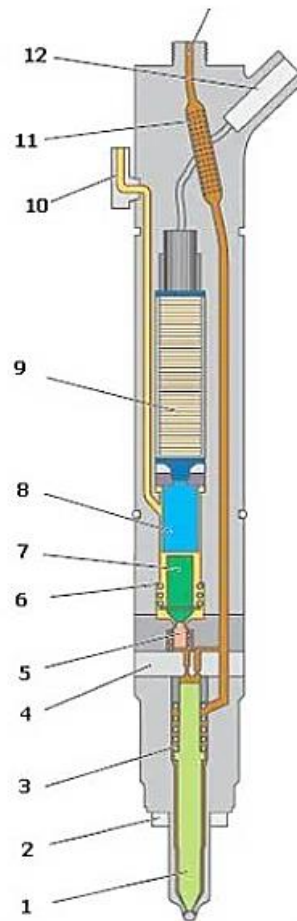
Конструкція п'єзофорсунки: 1 – голка форсунки; 2 – ущільнення; 3 – пружина голки; 4 – блок дроселів; 5 – перемикаючий клапан; 6 – пружина клапана; 7 – поршень клапана; 8 – поршень штовхача; 9 – п'єзоелемент; 10 – зливний канал; 11 – сітчастий фільтр; 12 – електричний роз'єм; 13 – нагнітальний канал.
